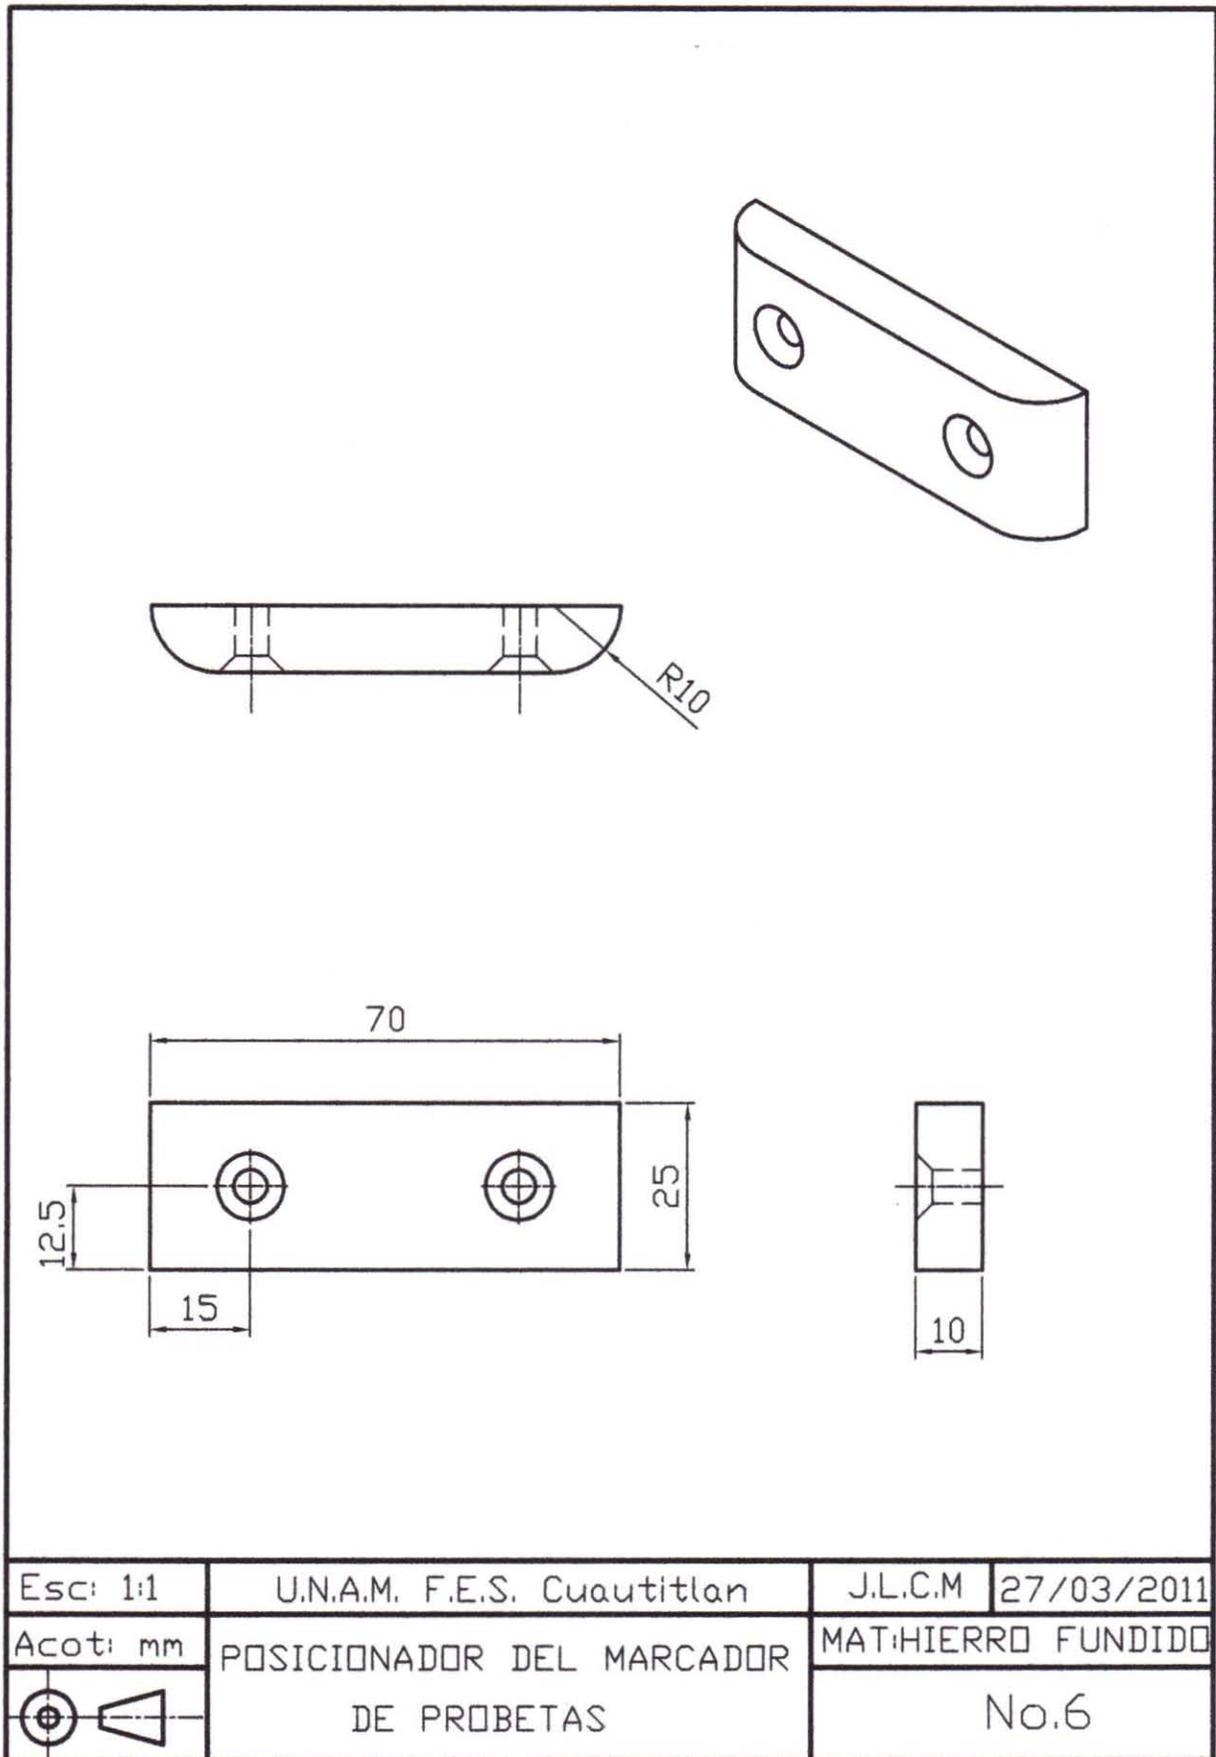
Dibujo de detalle del posicionador del dispositivo marcador de probetas
